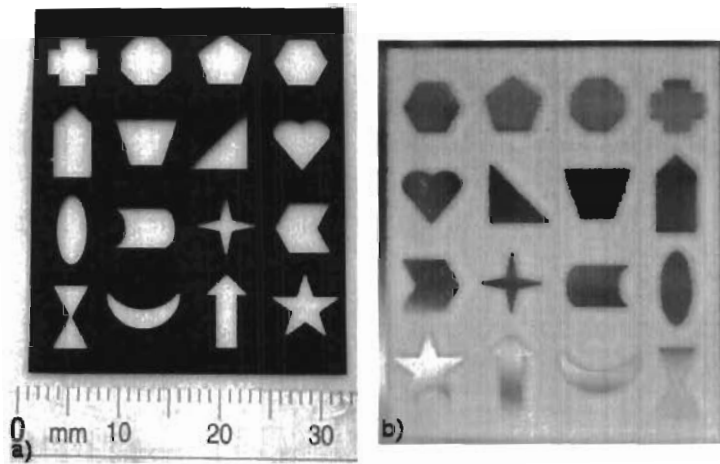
a) Molde (impresión láser en acetato). b) Estampa de PDMS.
